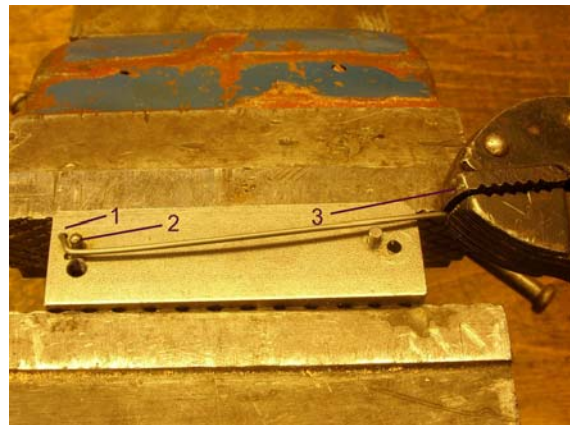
Abgekröpftes Drahtstück in Bohrung (1) stecken und Draht mit Zange (3) um Pfosten (2) biegen
